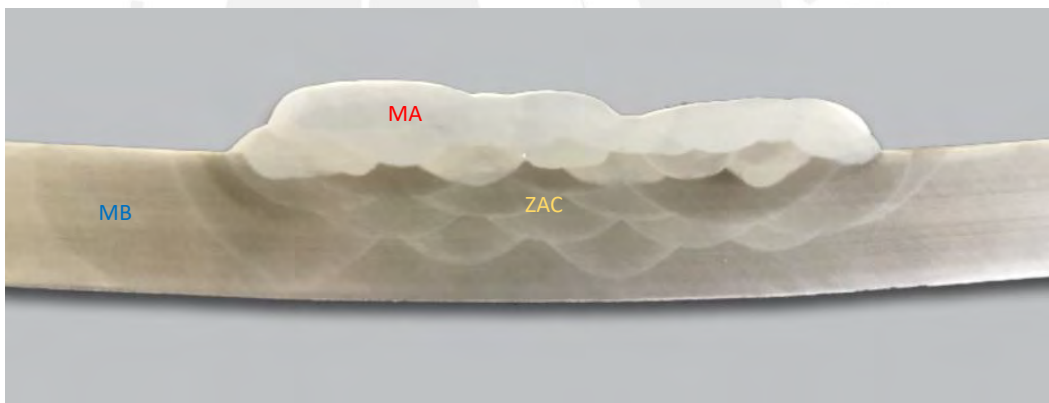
Macrografía de cupón de soldadura sin PWHT.
